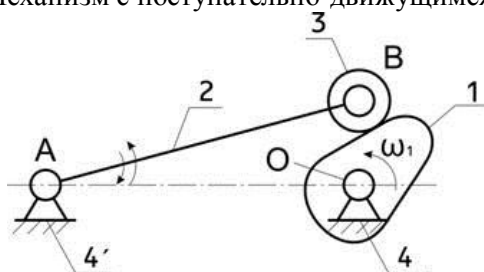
Кулачковый механизм с поворачивающимся толкателем
